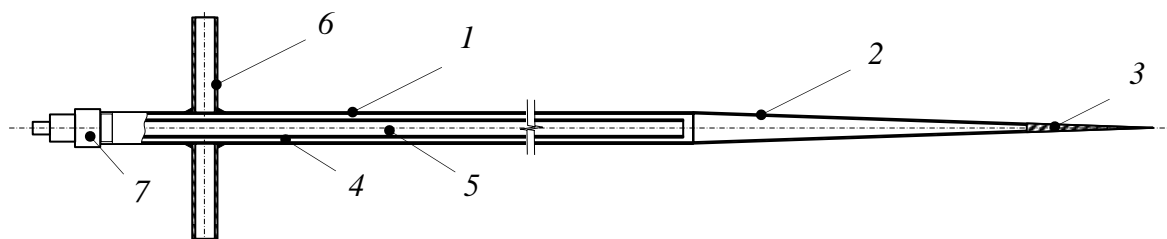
Конструкция экспериментального устройства: 1 – цилиндрическая часть корпуса; 2 – коническая часть корпуса; 3 – наконечник; 4 – паровой канал; 5 – артерия; 6 – рычаг; 7 – торцевая крышка
